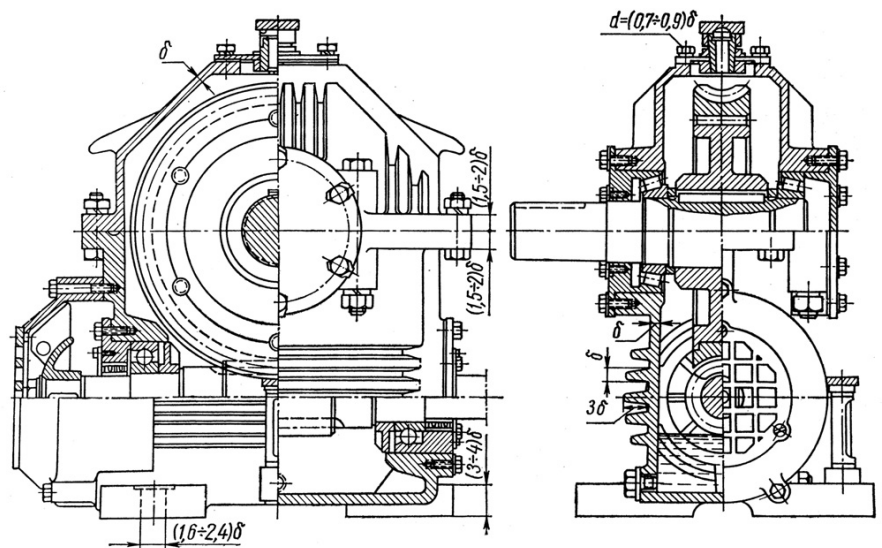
Reductor de tornillo sin fin-corona. Ejes montados sobre rodamientos en disposición ajustada. (Ref.1)
